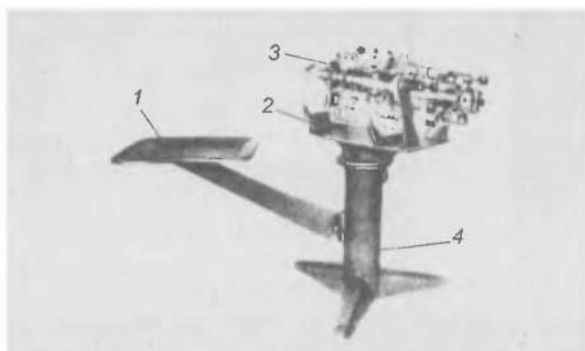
Универсальный стелды для разборки и сборки коробок передач грузовых автомобилей: 1 — подставка; 2 — ложемент-манипулятор; 3 — коробка передач; 4 — стойка
